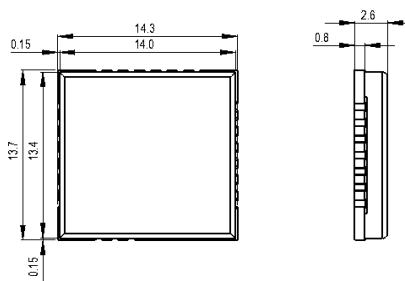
Габаритный чертеж ГеоС-ЗМ
